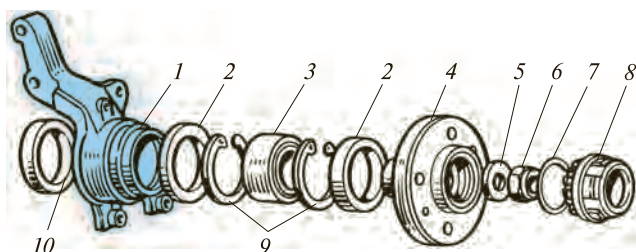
Поворотный кулак и детали ступицы переднего колеса:
